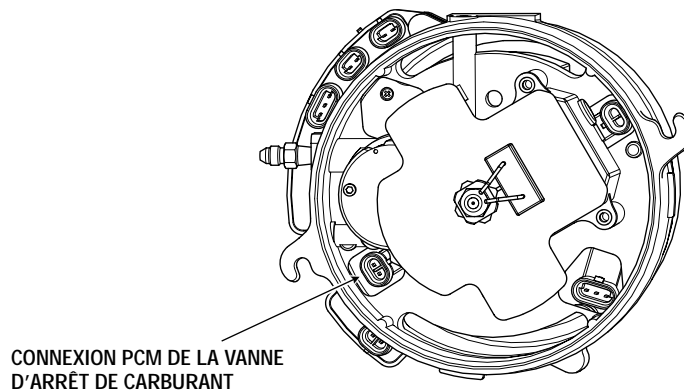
Connexion de la vanne d'arrêt de carburant du PCM
